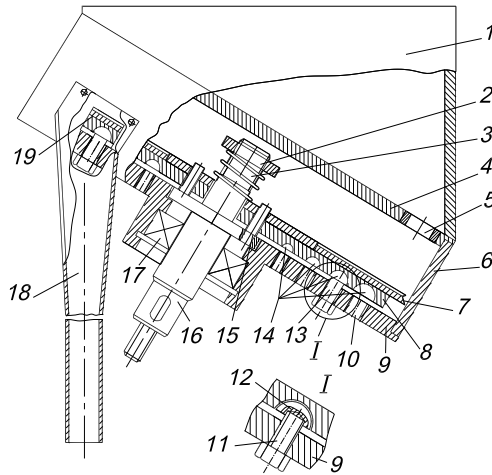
Конструктивна схема вібраційно-дискового висівного апарата: 1 – бункер для насіння; 2 – гайка; 3 – пружина; 4 – ділильник; 5 – отвір дозувальний; 6 – банка; 7 – висівний диск; 8 – проміжний диск; 9 – основа; 10 – отвори; 11 – болт; 12 – опора сферичної форми; 13 – змінні опори; 14 – комірки; 15 – штирі; 16 – приводний вал; 17 – підшипник; 18 – насіннепровід; 19 – бокове вікно
